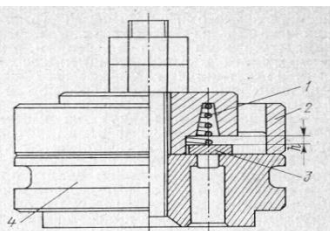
Клапан нагнетательный кольцевой пластинчатый четвертой ступени.
